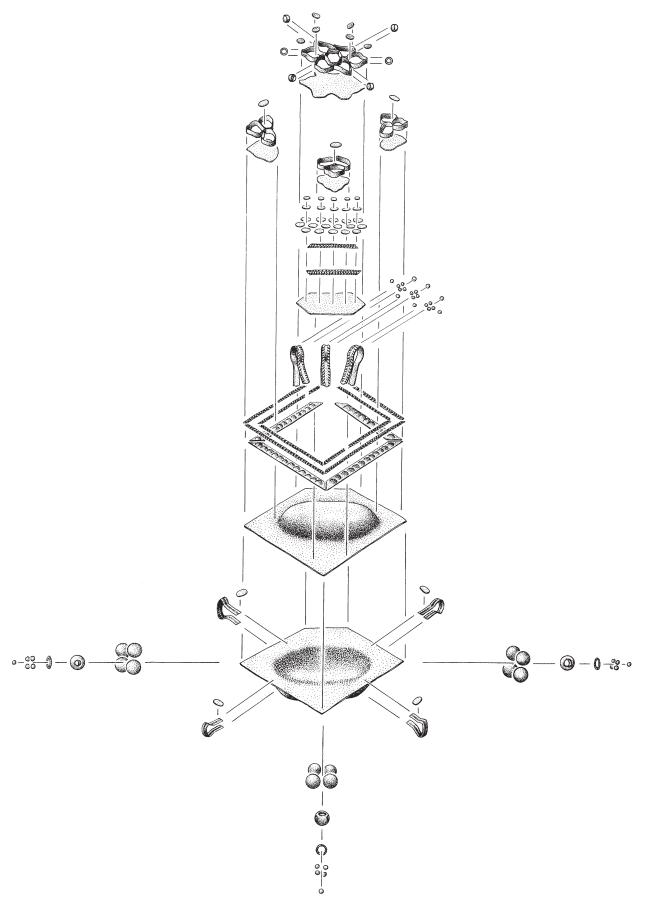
Kat. 23: Explosionszeichnung aller Einzelteile des rautenförmigen Goldanhängers, die in »Komposittechnik« zusammengelötet worden sind. – (Zeichnung M. Ober, RGZM).
